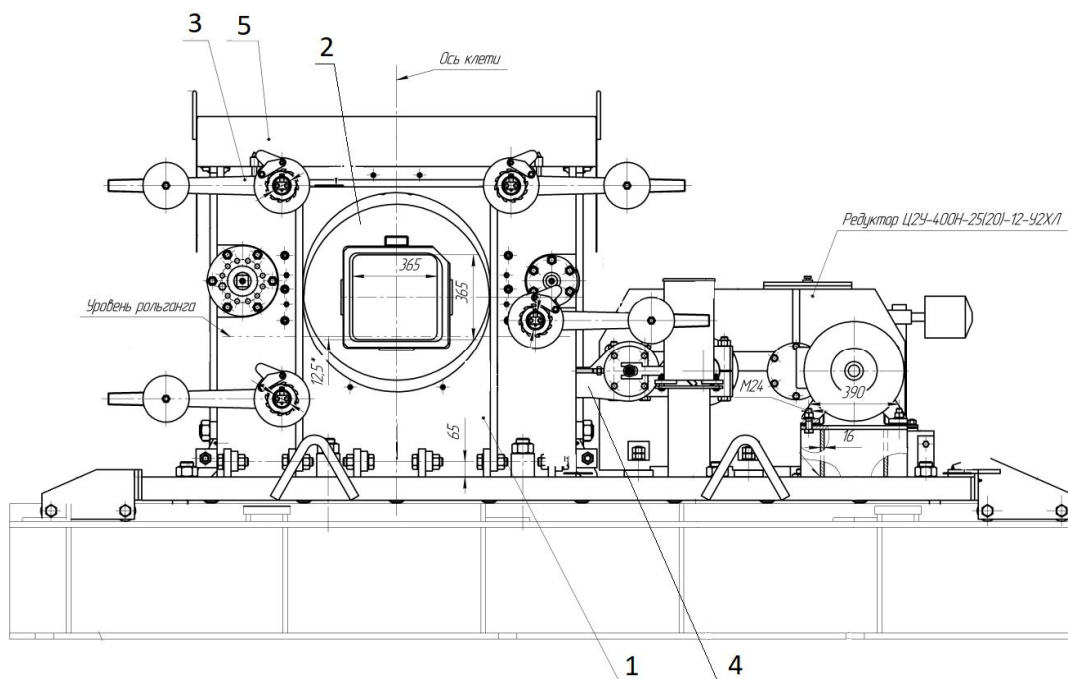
Универсальный кантователь крупносортового стана 600
